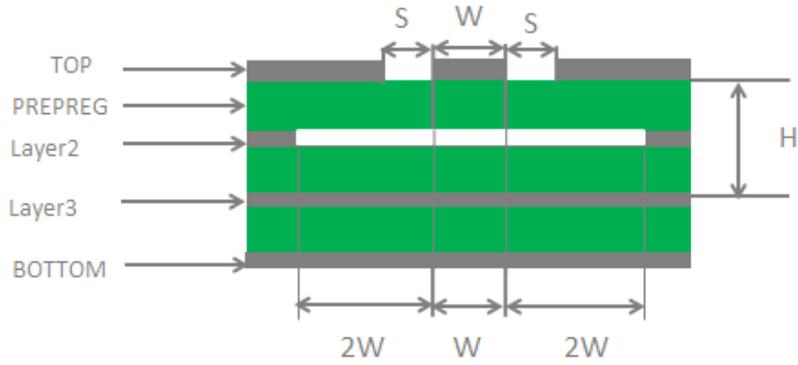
四层 PCB 板共面波导结构 (参考地为第三层)
